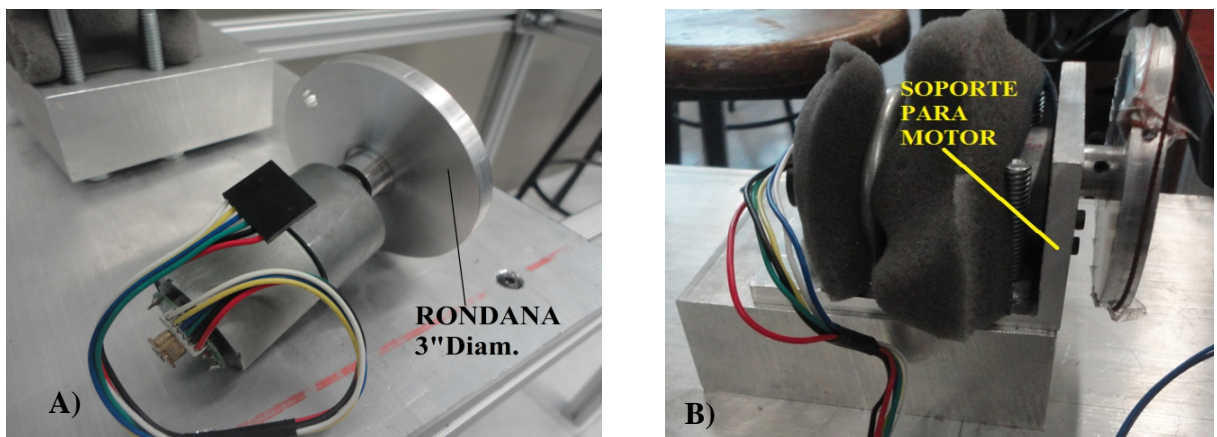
A) Rondana 3" diam. B) Montaje del motor
